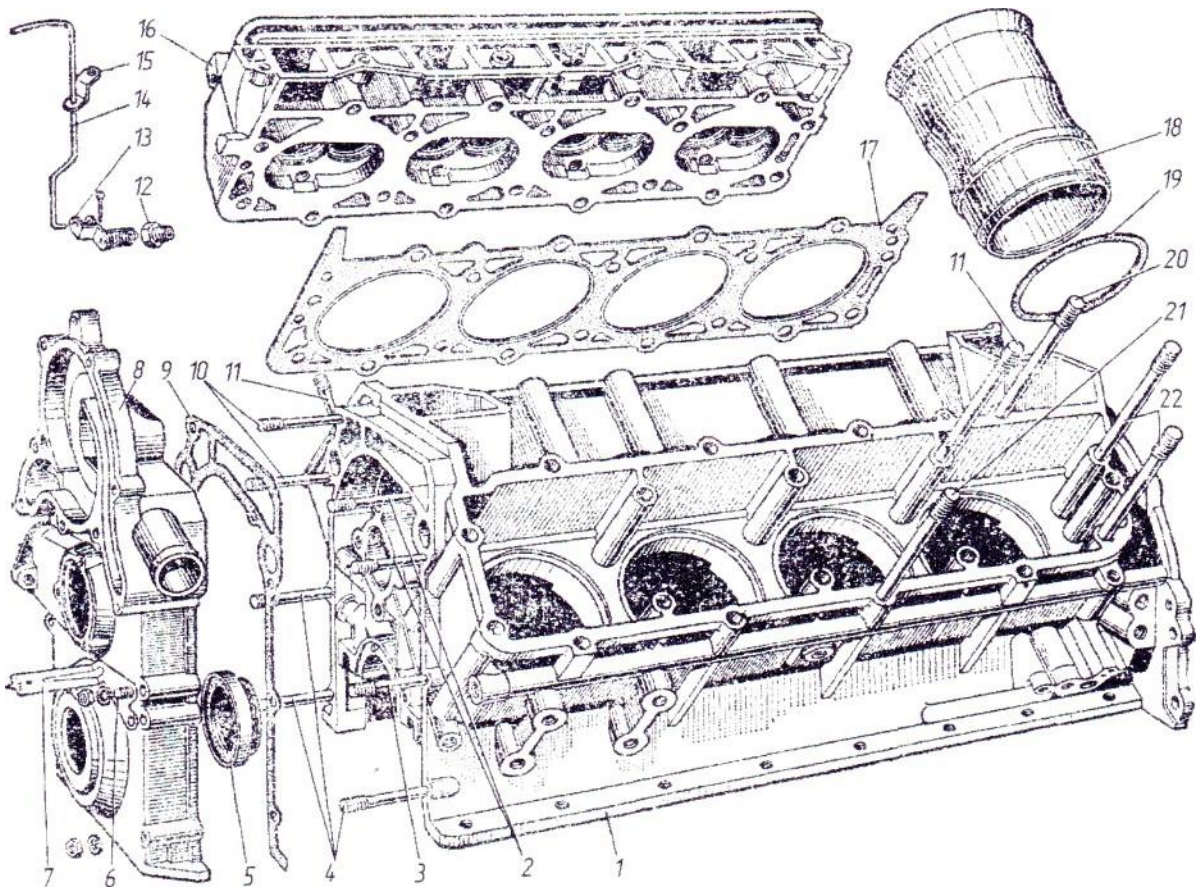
Блок і головка циліндрів V-подібного двигуна автомобіля: 11 Шпилька М11х1х208 кріплення головки циліндрів - 9 шт.; 20 - Шпилька М11х1х170 кріплення головки циліндрів - 9 шт.; 21 - Шпилька М11х1х108 кріплення головки циліндрів - 8 шт.; 22 - Шпилька М11х1х195 кріплення головки циліндрів - 10 шт.; Гайка М11х1 - 36 шт.; Шайба 11,5 - 35 шт.
